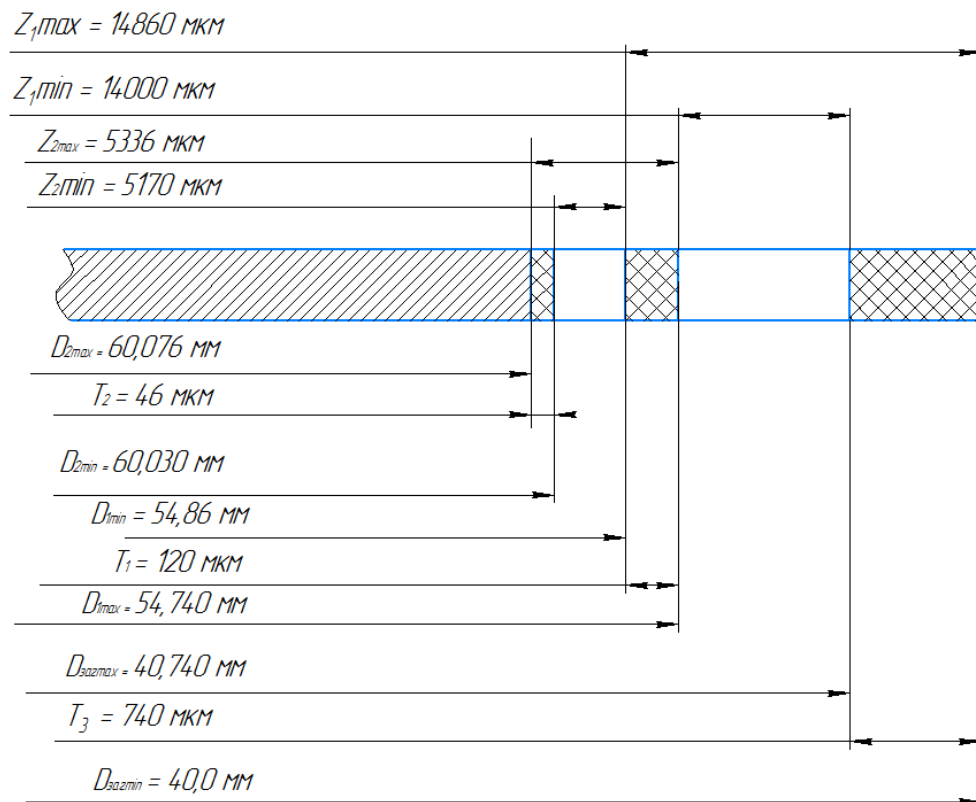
Схема графічного розташування припусків та допусків на обробку поверхні Ø60F8
